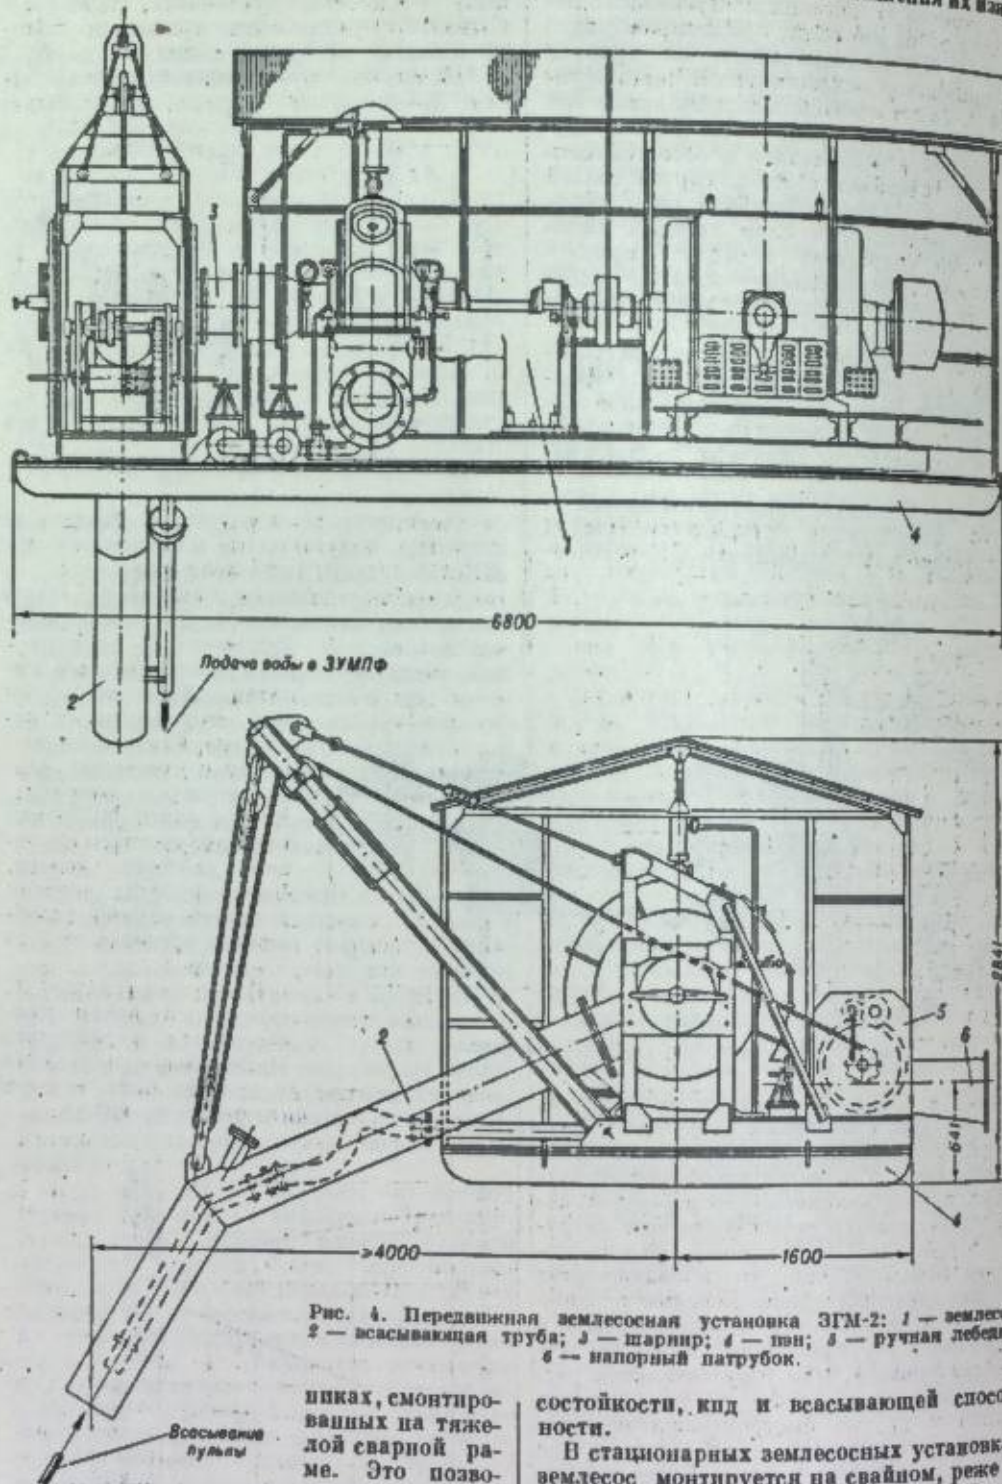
Передвижная землесосная установка ЗМ-2: 1 — землесос; 2 — всасывающая труба; 3 — шарнир; 4 — пил; 5 — ручная лебедка; 6 — напорный патрубок.
